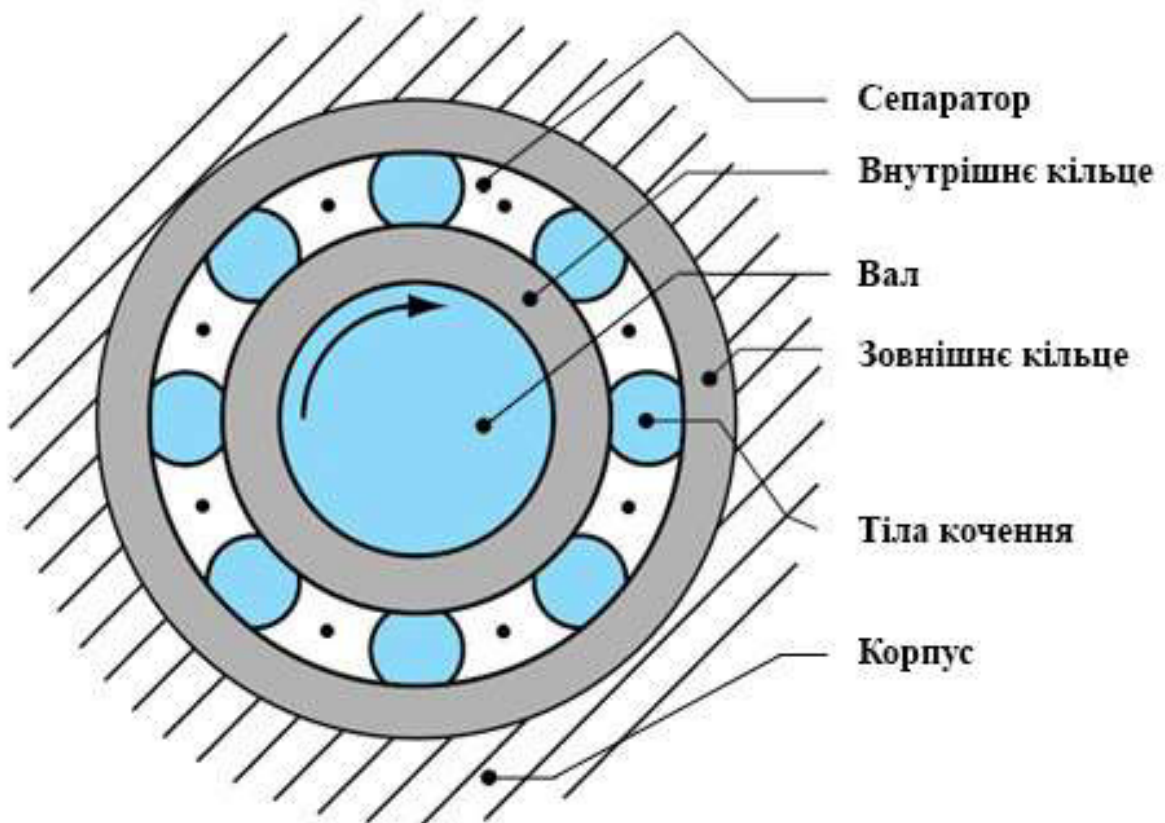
Принципова схема опори з підшипником кочення
